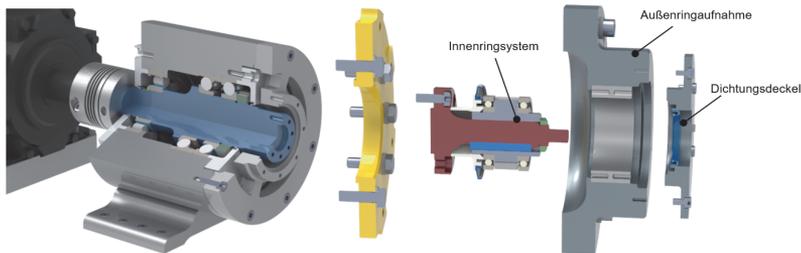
Detailansicht des Prüfaufbaus aus /5/
